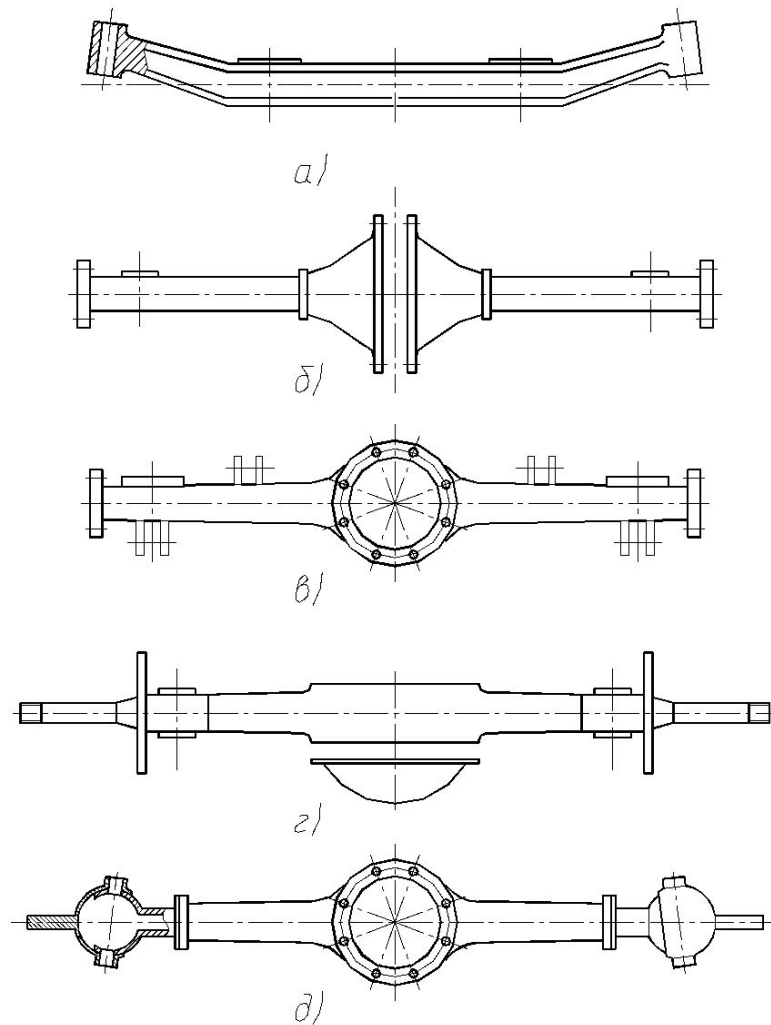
Неразрезные балки мостов: а – управляемый, ведущие: б – разъемный, в – неразъемный штамповано сварной, г – неразъемный литой, д – комбинированный
